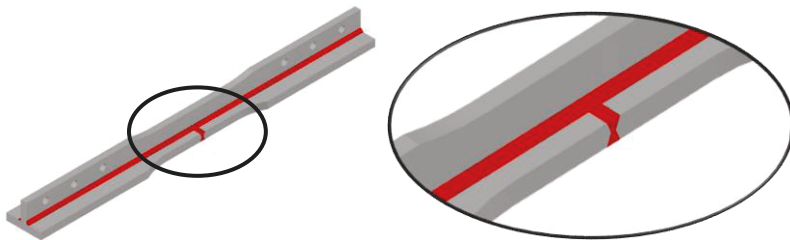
Kleinteil T-Probe mit Stumpfstoß [116]
